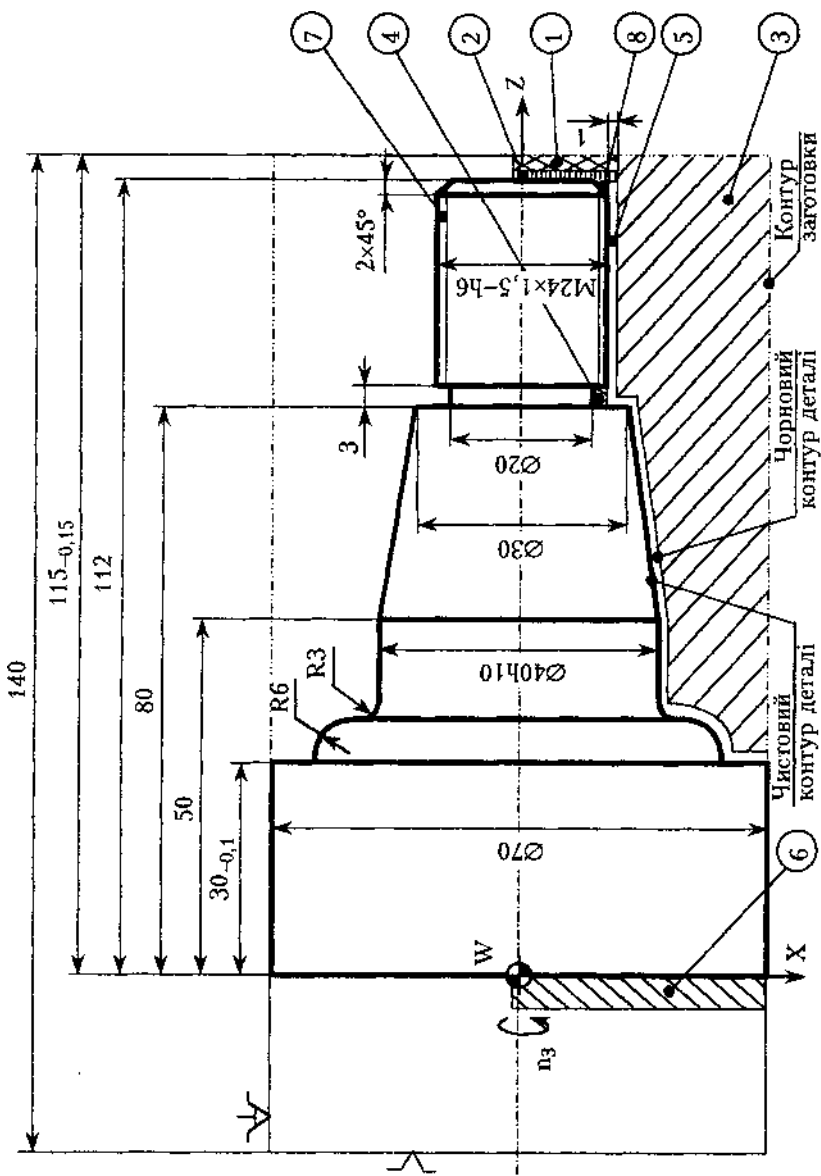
Креслення обробленої деталі з позначеними шарами припусків
